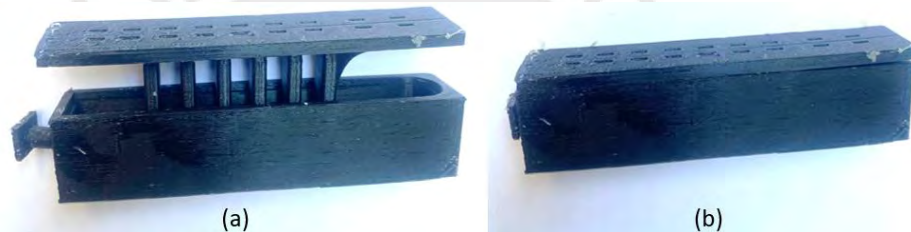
Molde impreso: (a) Vista representativa de unión, (b) Partes unidas.
